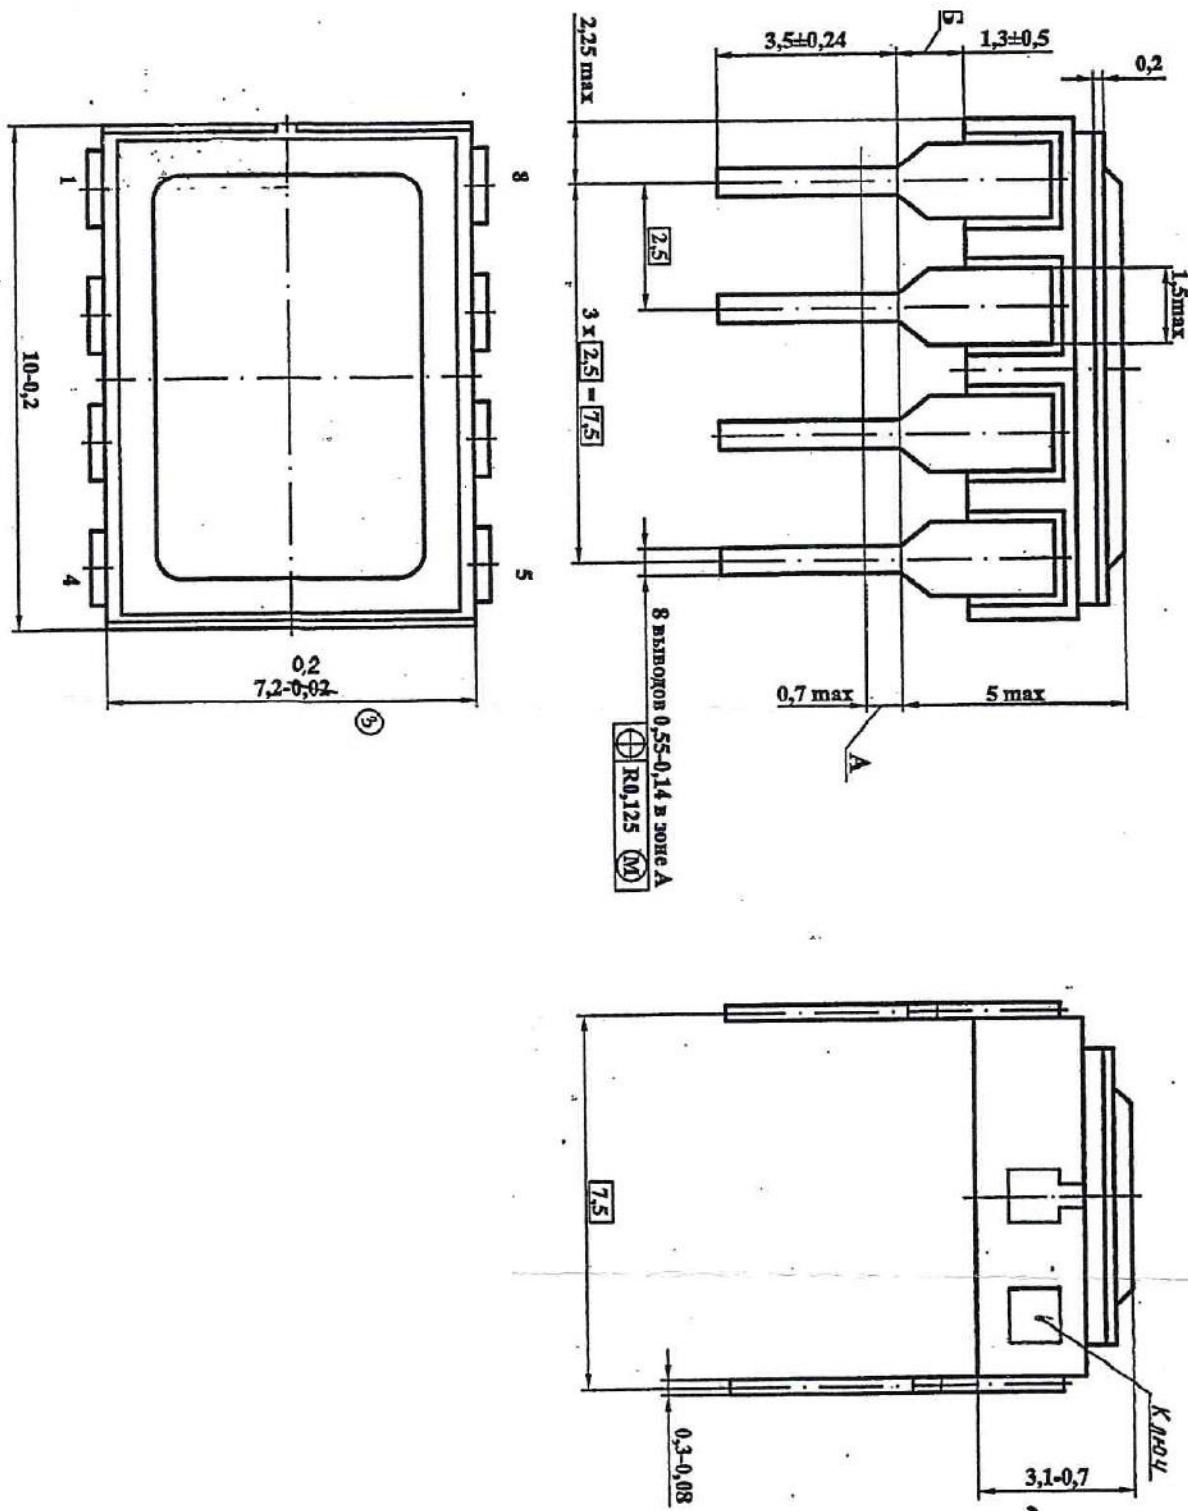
Габаритный чертеж корпуса 2101.8-7
